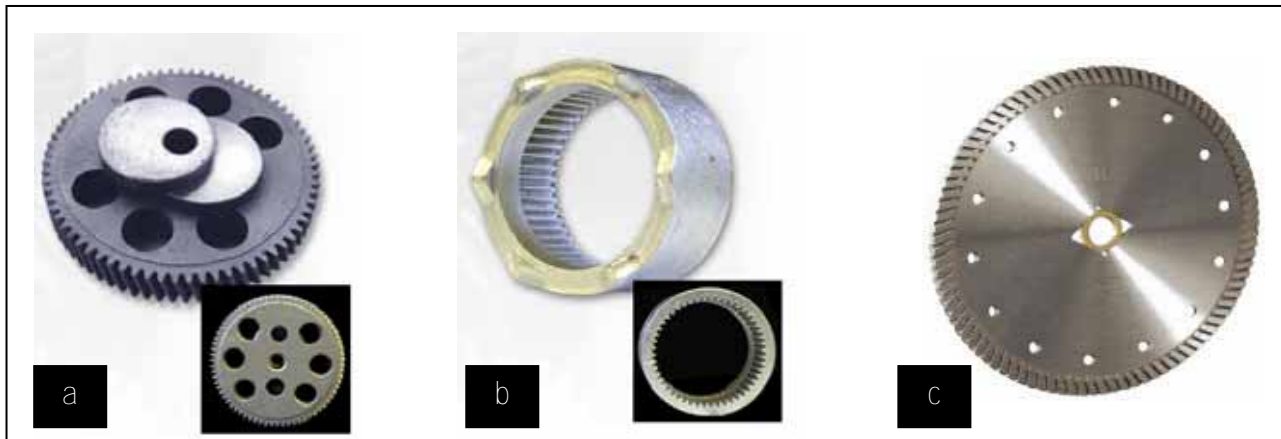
Engranajes fabricados mediante técnicas PM ¹⁹⁵.
